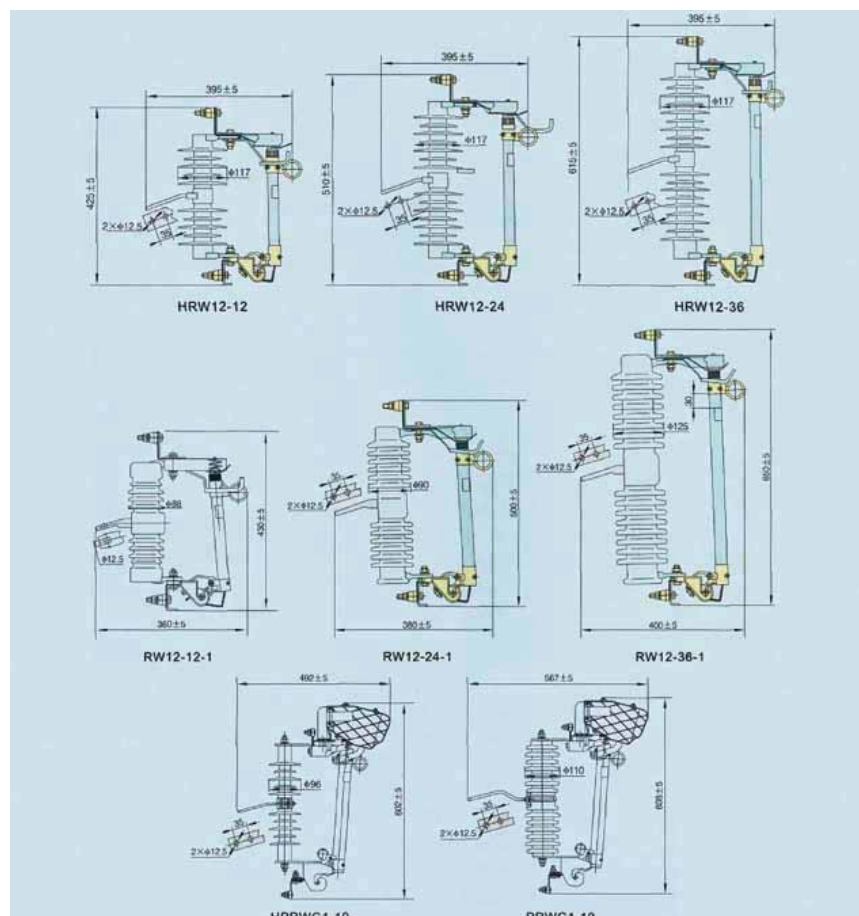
Внешний вид и размеры откидывающегося плавкого предохранителя
